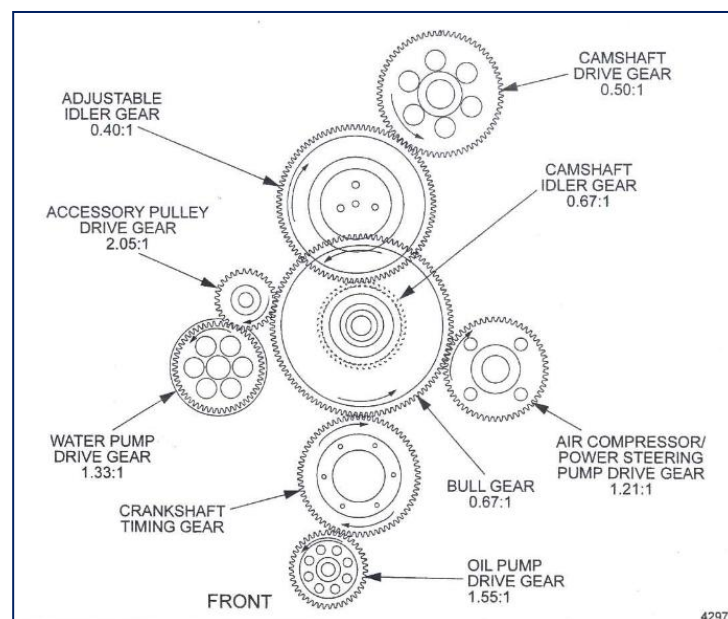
Engranajes de la Distribución del Motor DDS60.³¹
